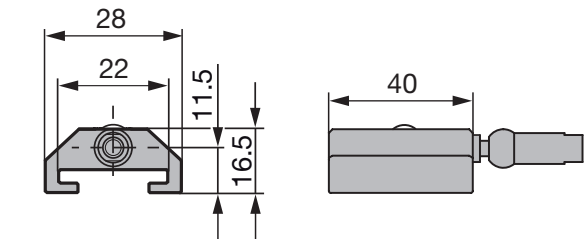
Dimensions de montage du capteur de position BTL5-T-2814-1S
